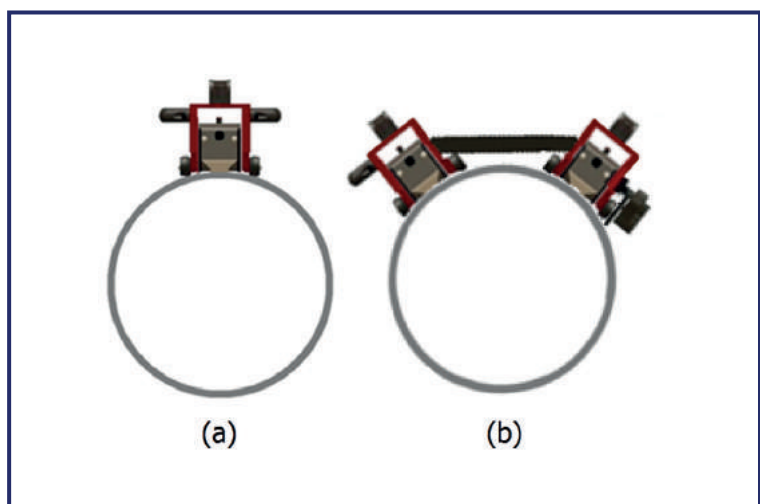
Configuraciones posibles del escáner MRUT para inspección axial de tubería. (a) 1 sensor, (b) 2 sensores
